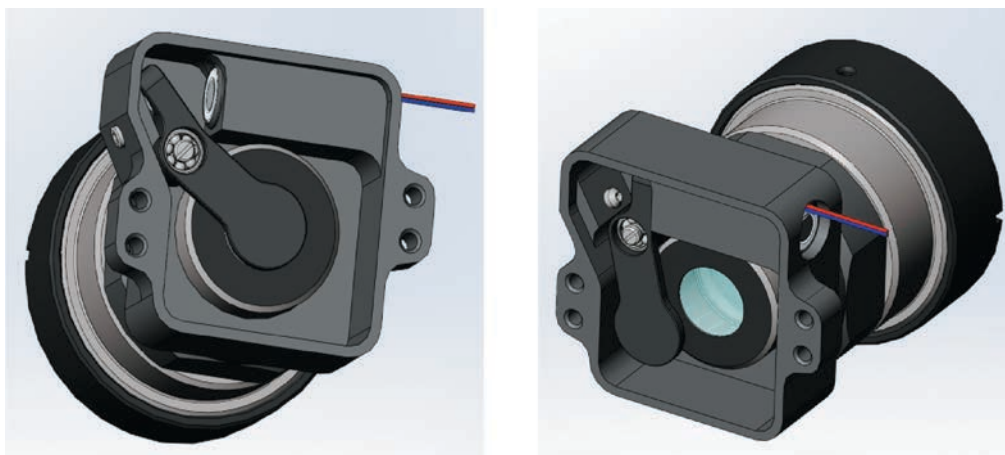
Узел крепления объектива с блендой и калибровочным затвором
